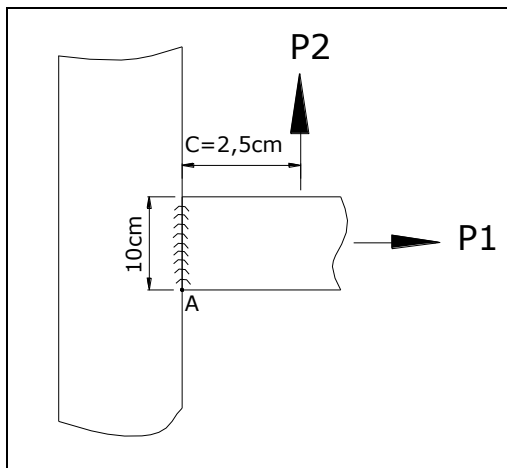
Carga de flexión para la soldadura.
